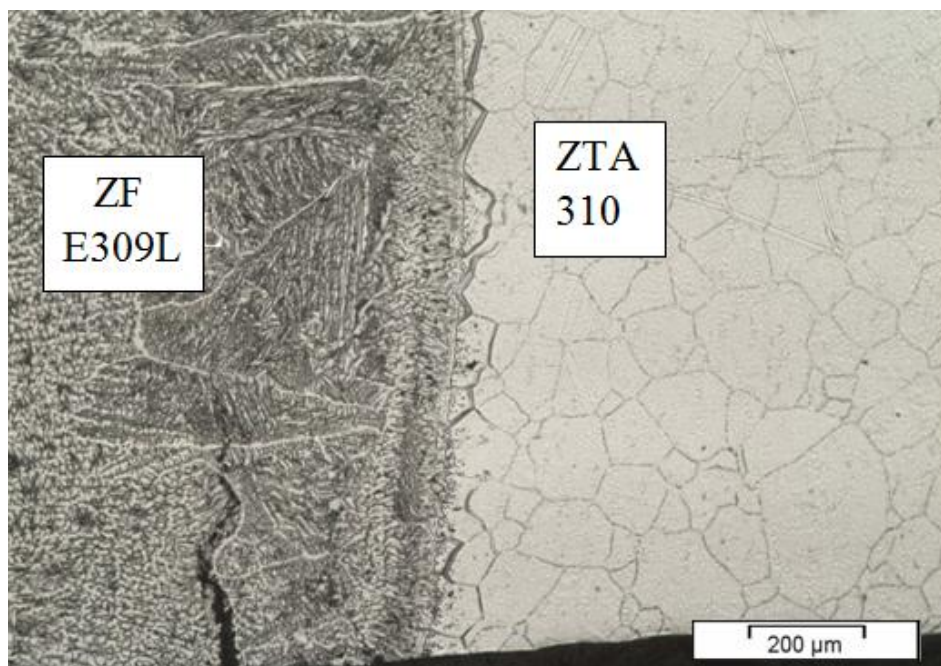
Trinca na zona fundida do metal de adição E309L soldada com o metal base 310. Ataque eletrolítico: Ácido Oxálico
